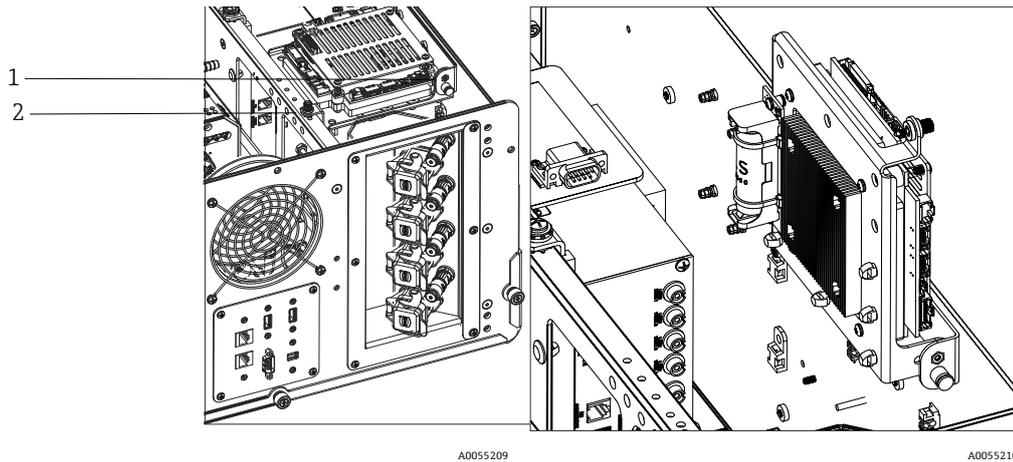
Rückansicht mit Steuerungsplatine in geöffneter Position
